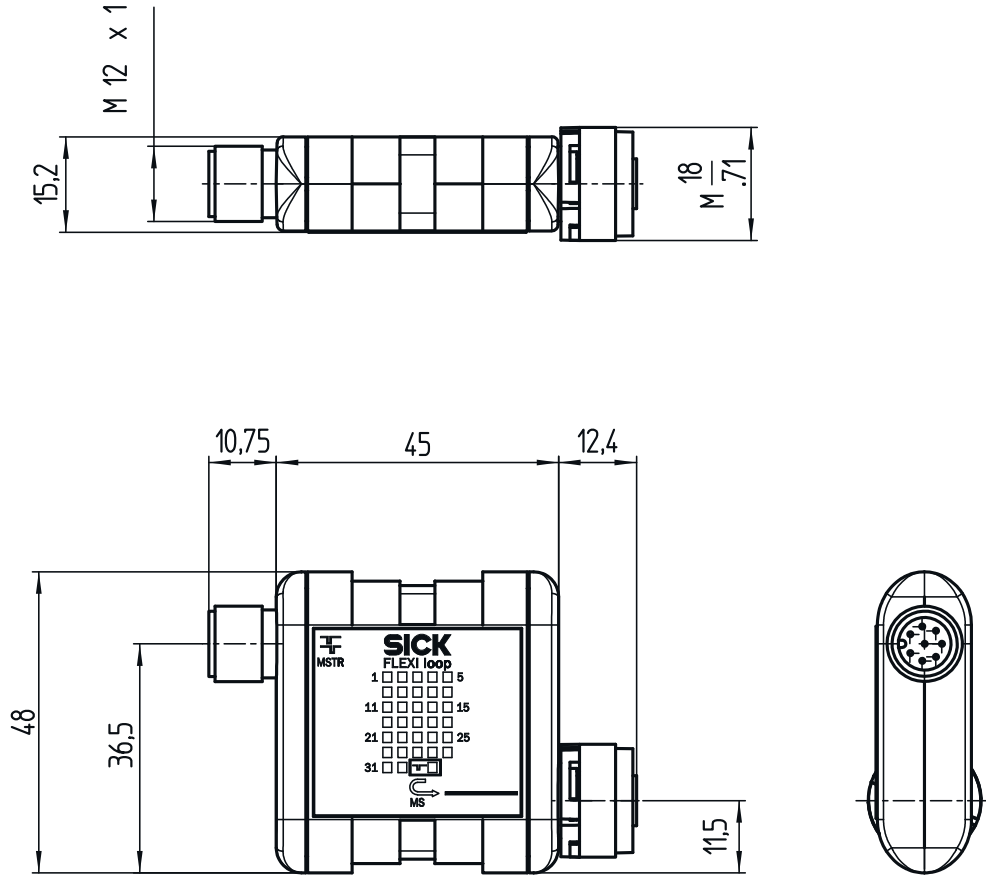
Plan coté des accessoires Flexi Loop FLA-MSTR00001 (mm)
